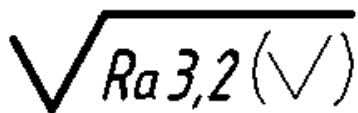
Обозначение шероховатости одинаковой для части поверхностей
